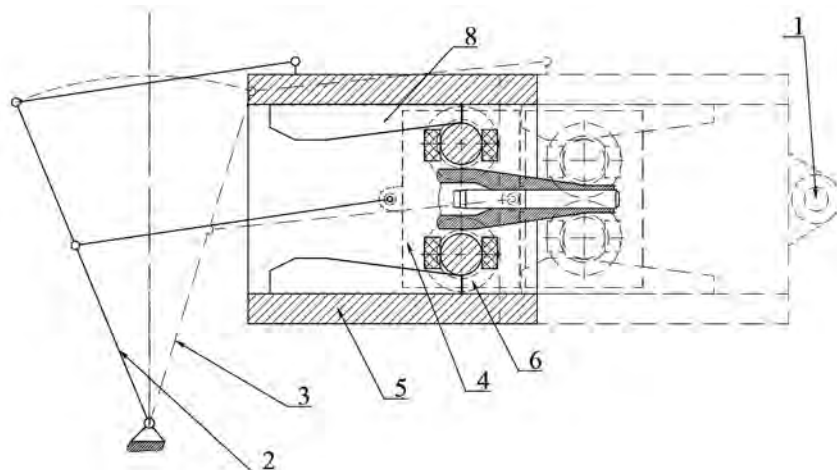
Схема, показывающая совместное движение корпуса с планками и сепаратора:
